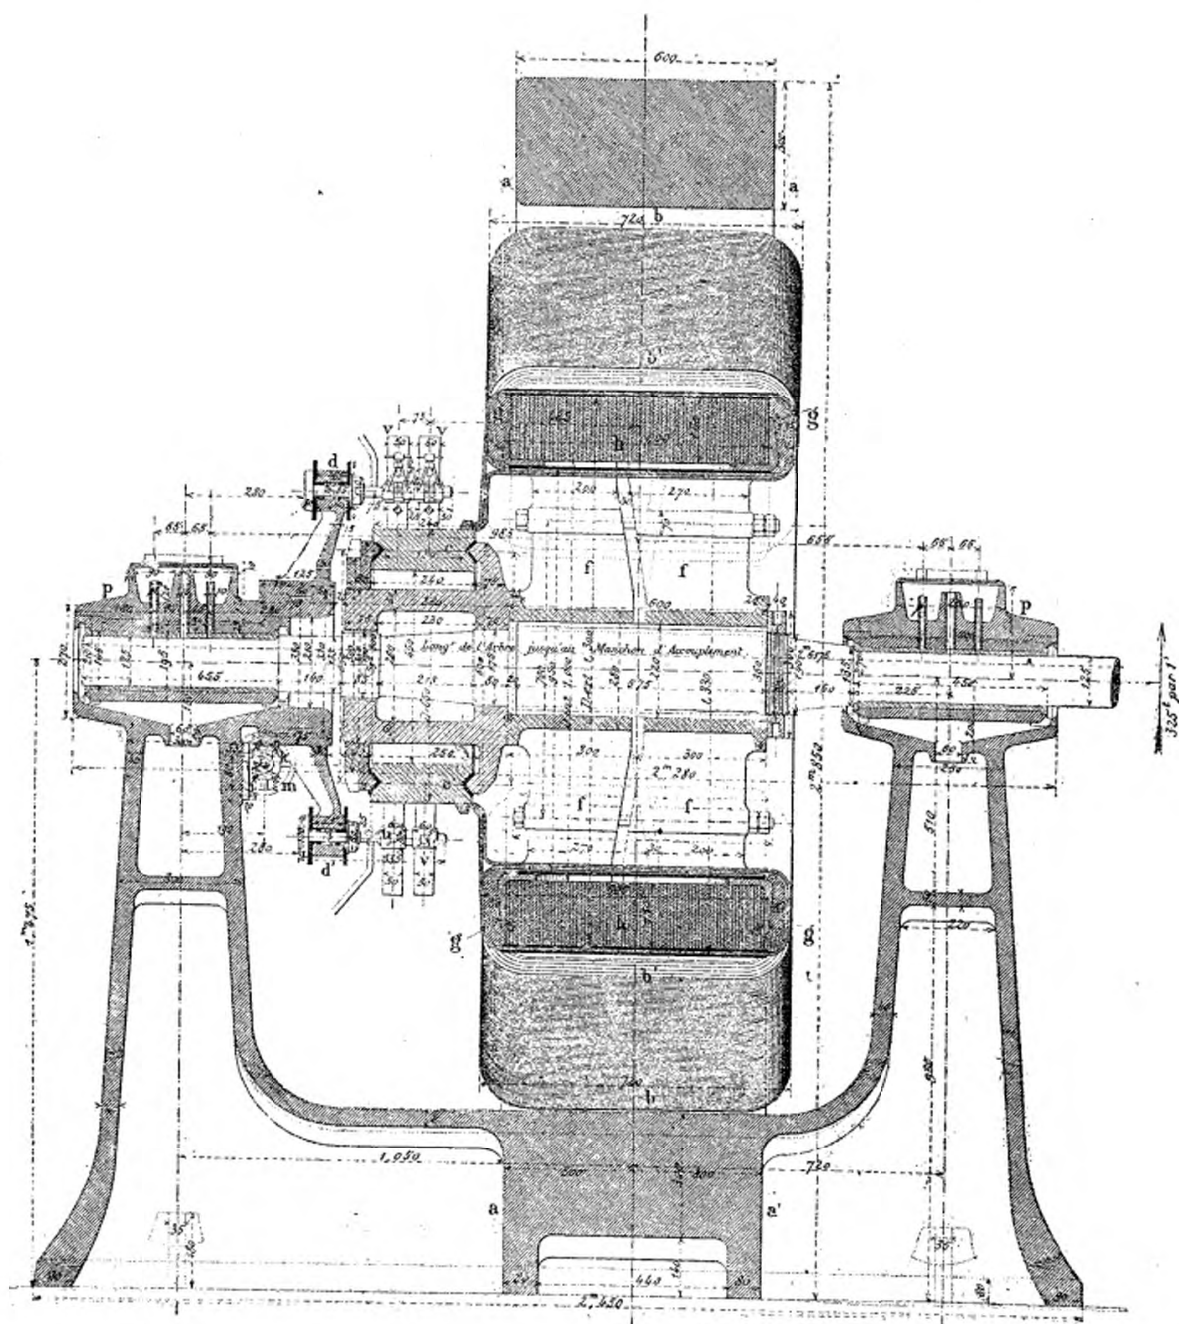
Dynamo construite par les ateliers d'Oerlikon.
